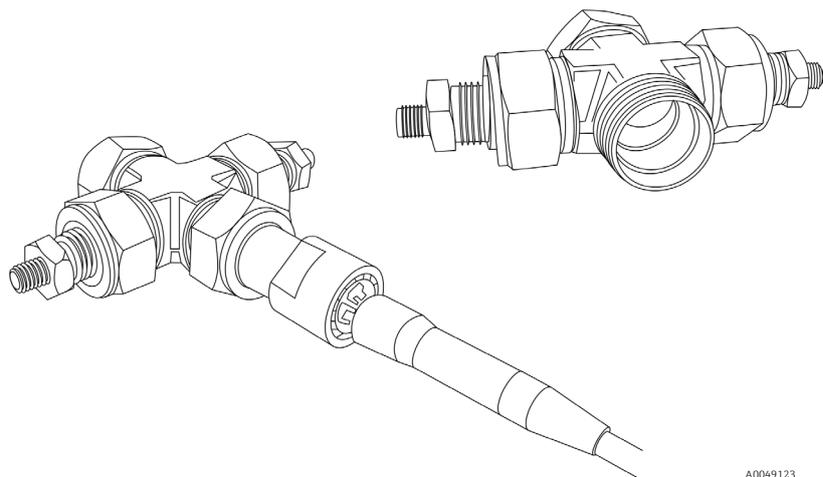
Rxn-30-Sonde in 1in-Kreuzanschlussstück mit Standardklemmverschraubung eingesteckt
